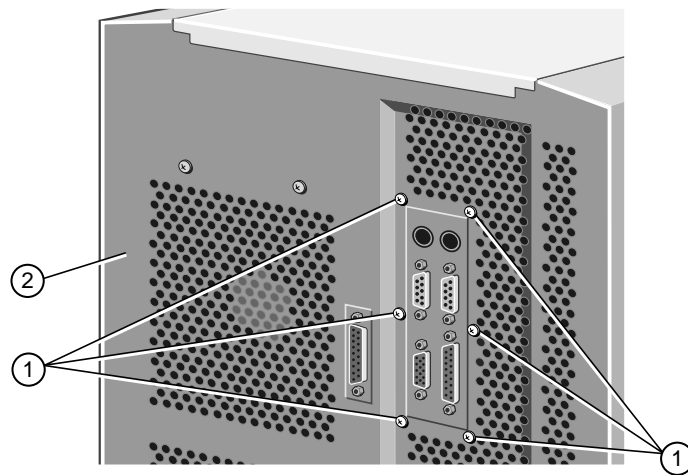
Schrauben der Platine auf der Hintertafel
